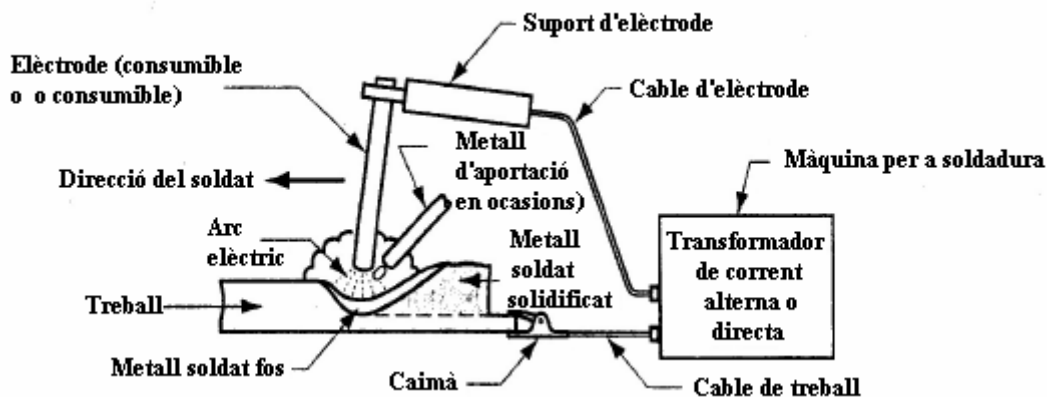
Configuració bàsica i circuit elèctric d'un procés de soldadura amb arc elèctric.
